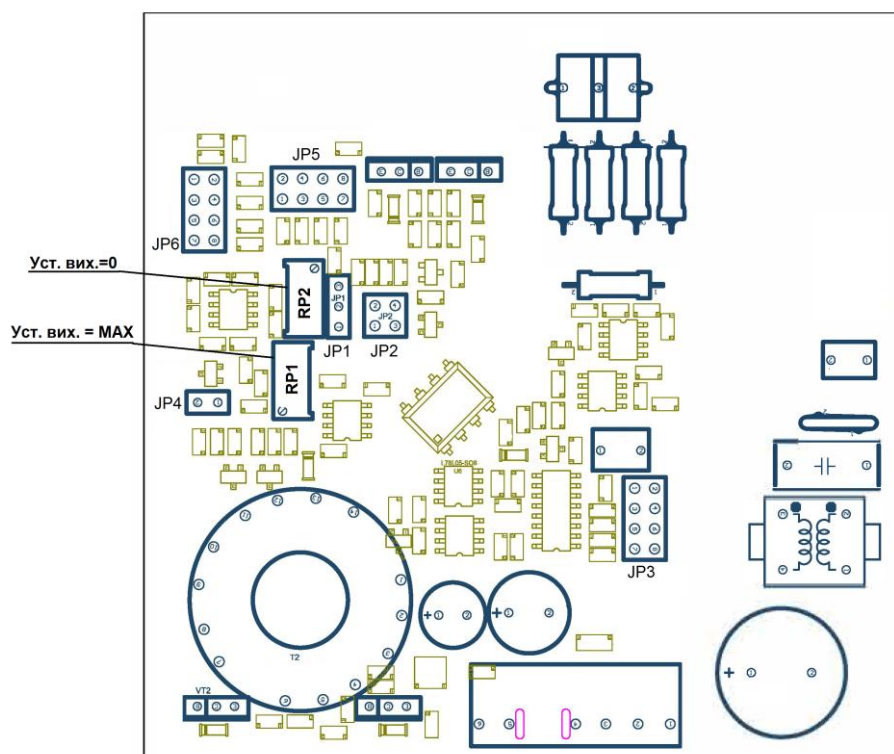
Схема розміщення елементів регулювання та налаштування ПНС-1 (для приладів з платою ПРМК.758740.1034)
